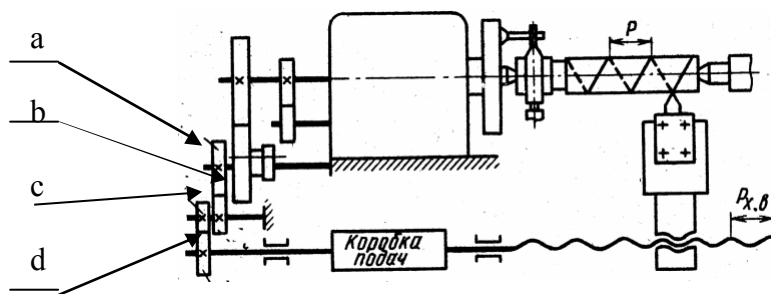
Резьбонарезная цепь токарно-винторезного станка.
